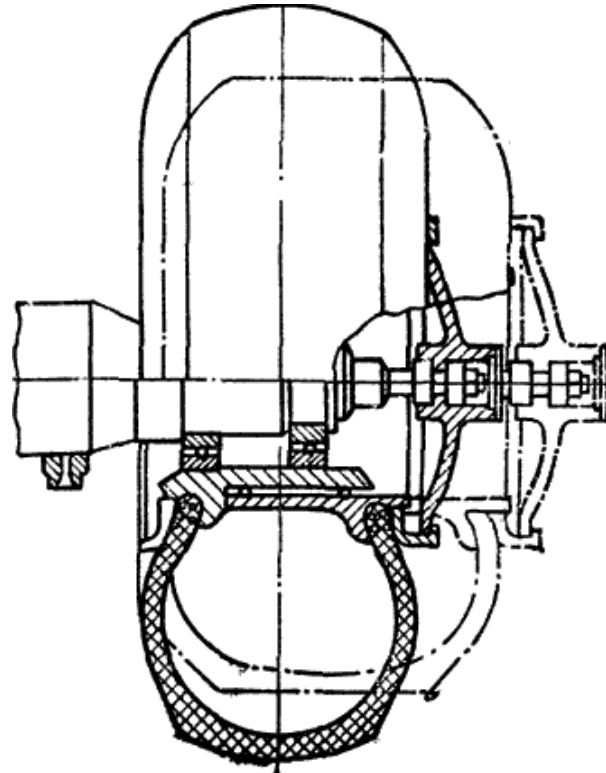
Адаптивный движитель с изменяемой формой колеса
